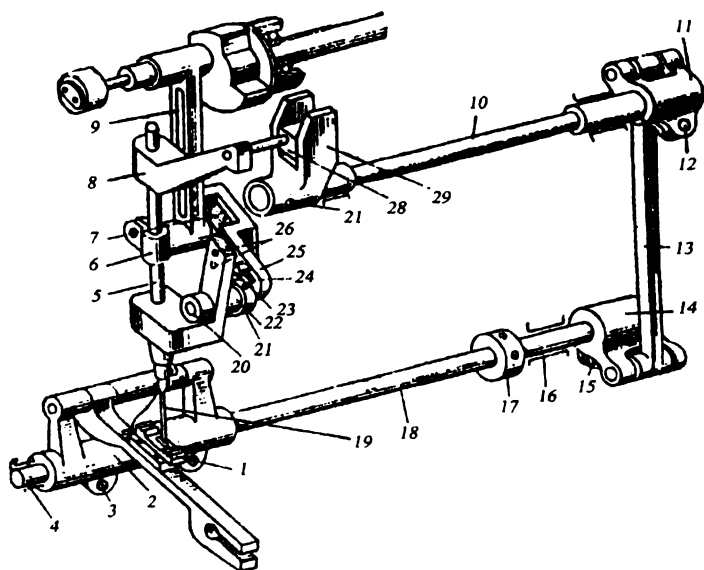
Конструкция механизма движения иглы машины 597-М кл. ОЗЛМ
